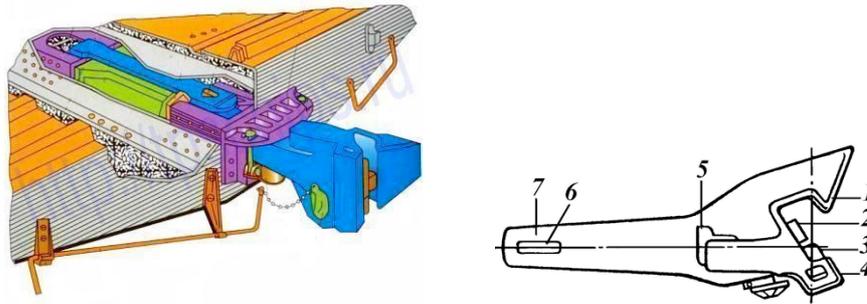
Корпус автосцепки в сборе: 1 – большой зуб; 2 – замкодержатель; 3 – замок; 4 – малый зуб; 5 – выступ; 6 – отверстие для клина; 7 – торец хвостовика
